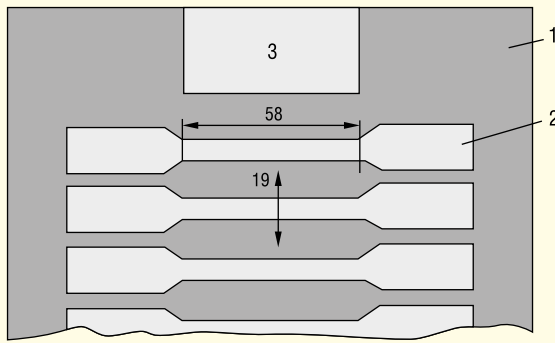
Пластина для виготовлення тест-зразків для вимірювання пластичності гальванопокриттів: 1 – фоторезист; 2 – оголена металева поверхня для осадження півки гальванопокриття; 3 – металева поверхня для приєднання до катодної штанги
